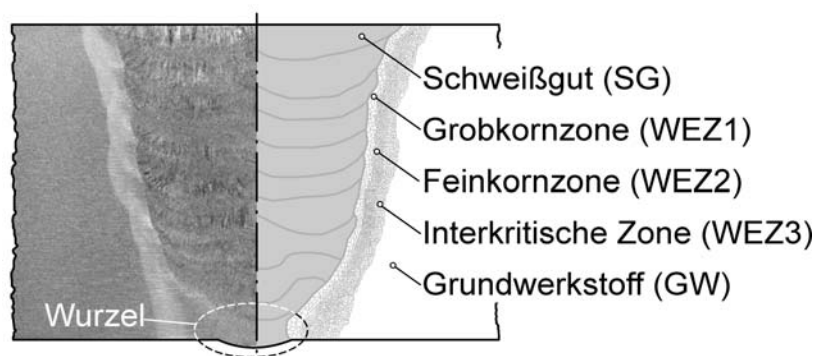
Klassische Einteilung einer Schweißnaht in fünf Zonen.
